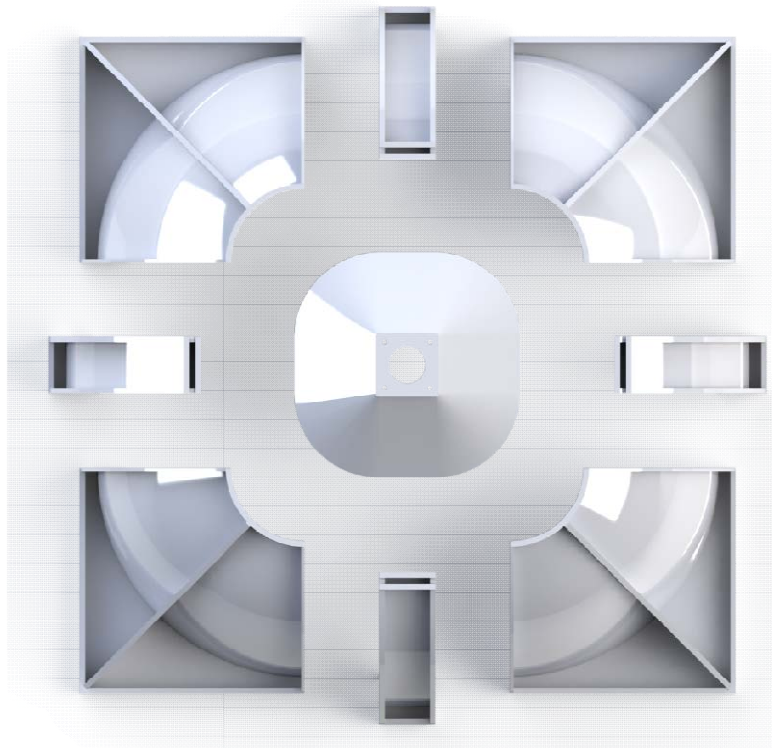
Ensamblaje del domo explosionado desde vista superior.
